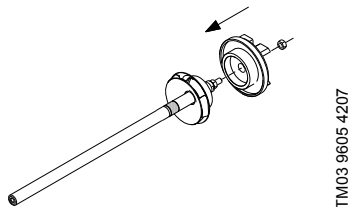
Установка рабочего колеса и державки на вертикальный вал
